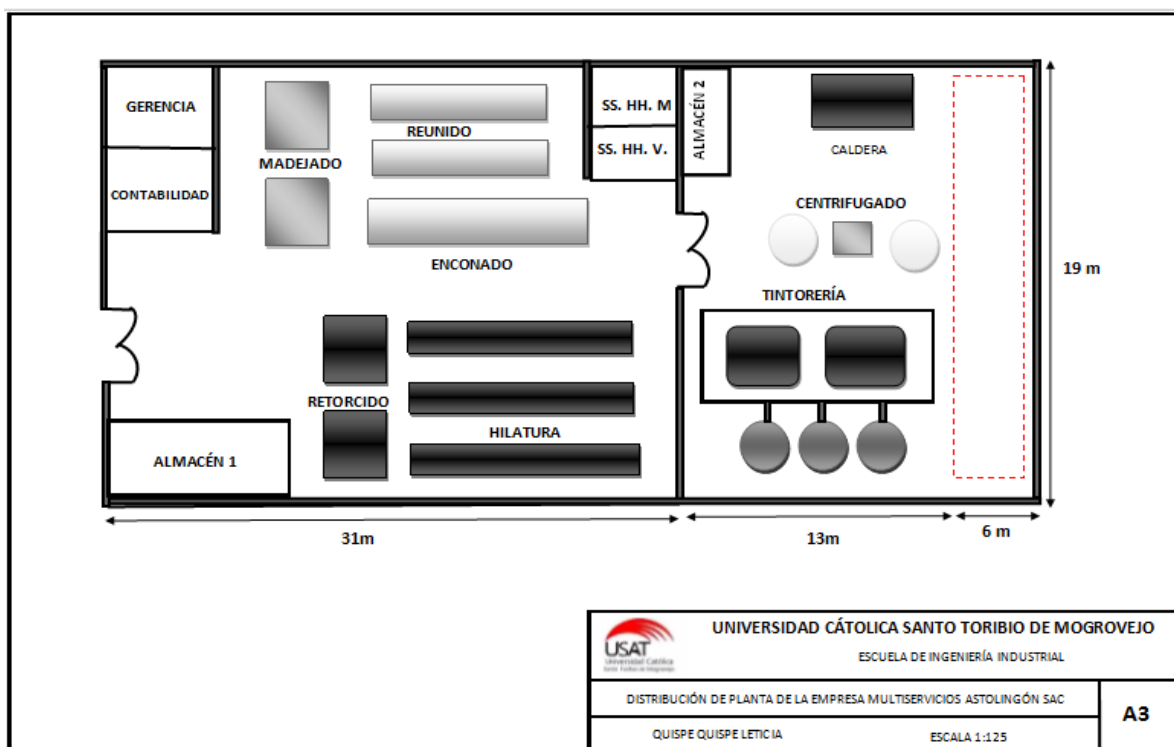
Plano de distribución de la planta Multiservicios Astolingón
